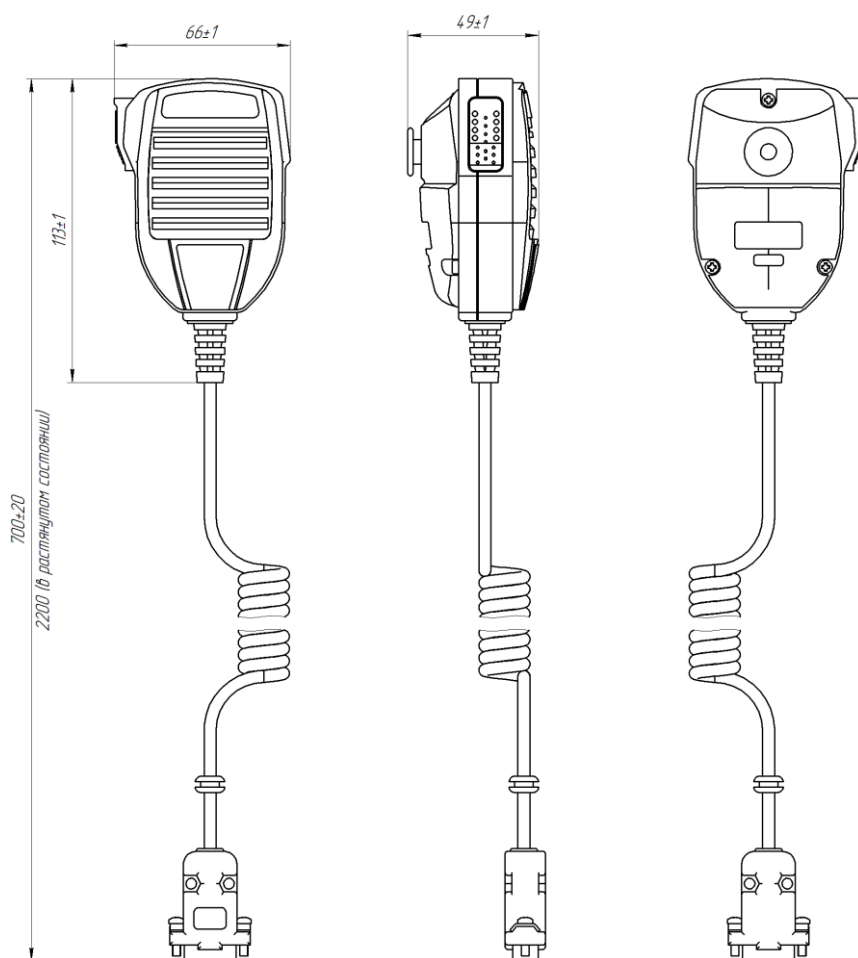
Габаритные и установочные размеры МТТ
